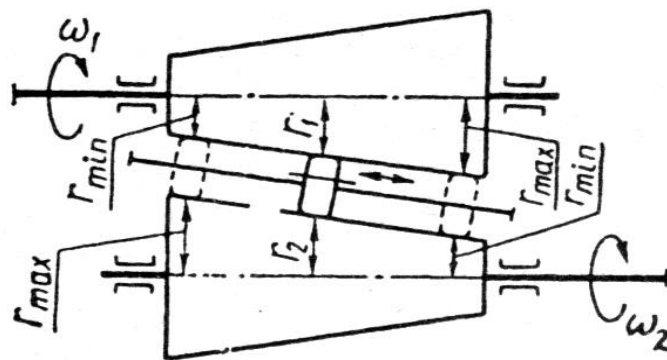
Схема конусного варіатора з проміжними дисками
